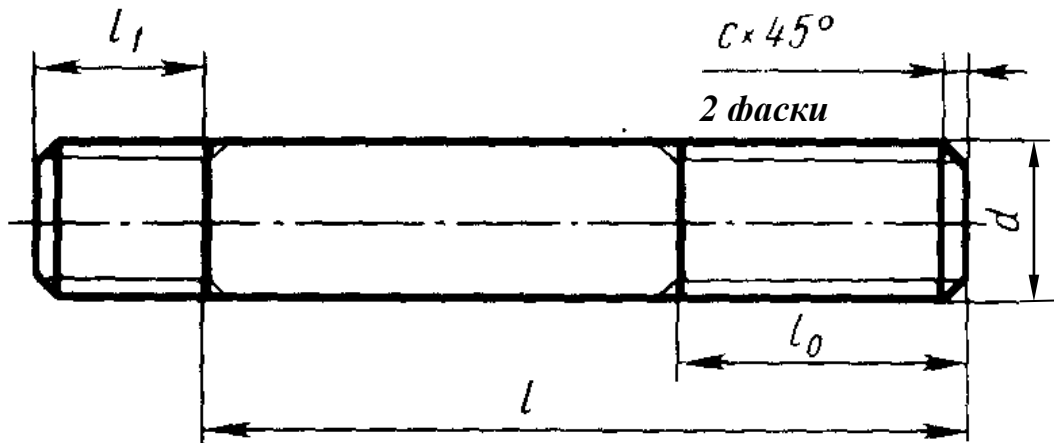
Шпилька общего применения для деталей с резьбовыми отверстиями
